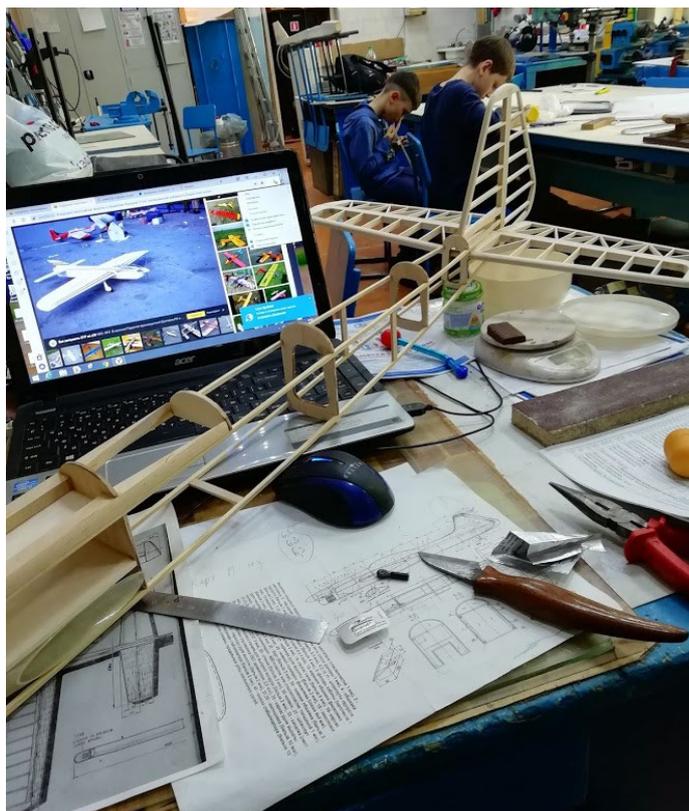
Сборка фюзеляжа, киля и стабилизатора
